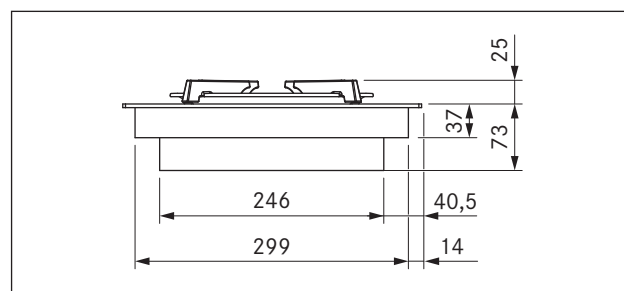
Dimensões do aparelho CKG, vista frontal
